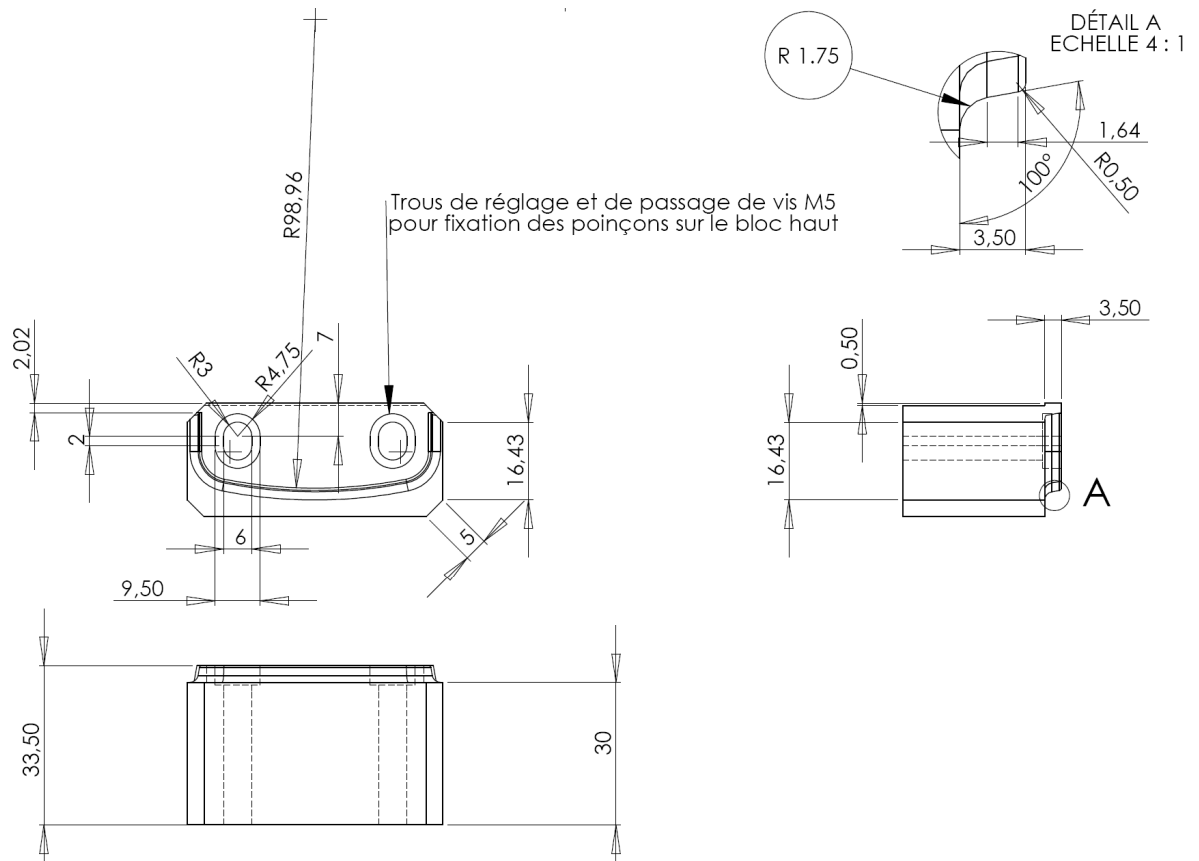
Plan des poinçons pour l'outil de rayonnage
